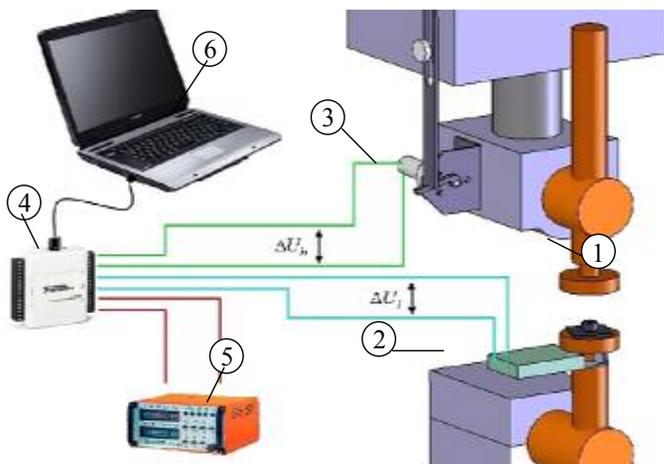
Установка для контроля качества рельефной сварки
